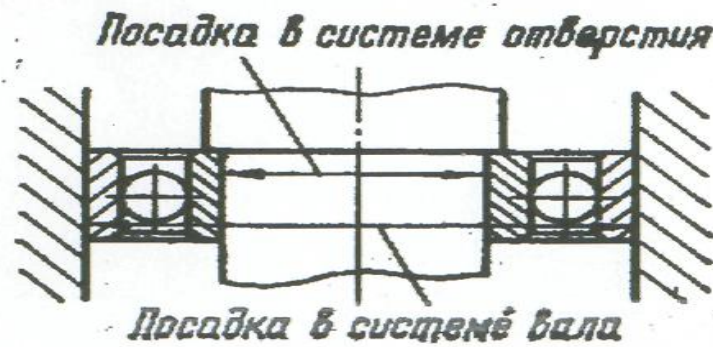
Посадки в СА и СВ колец подшипников качения
